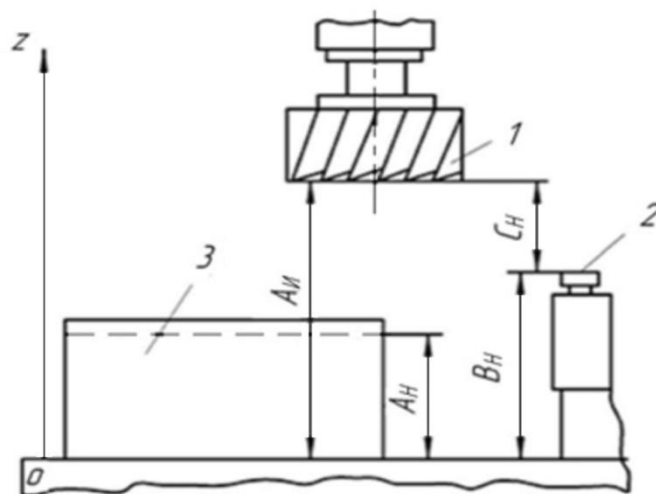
Схема размерной настройки инструментов многоцелевого станка с ЧПУ по оси Z
